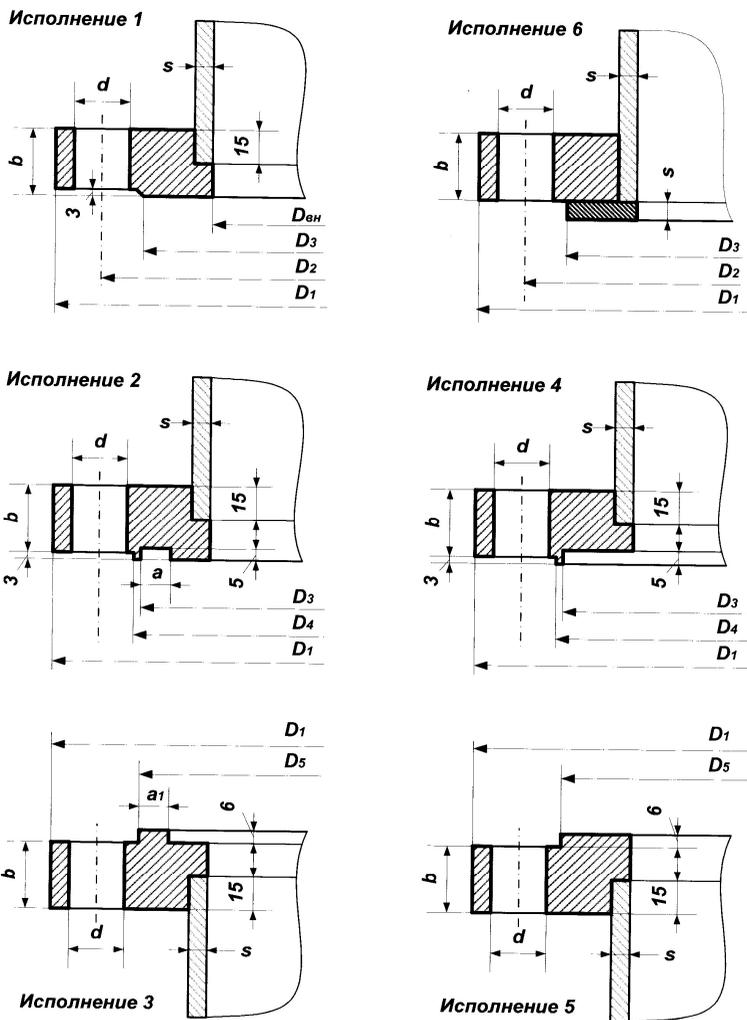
Конструкции и размеры стальных плоских приварных фланцев для сосудов и аппаратов по ГОСТ 28759.2-90 (к табл. 24)
